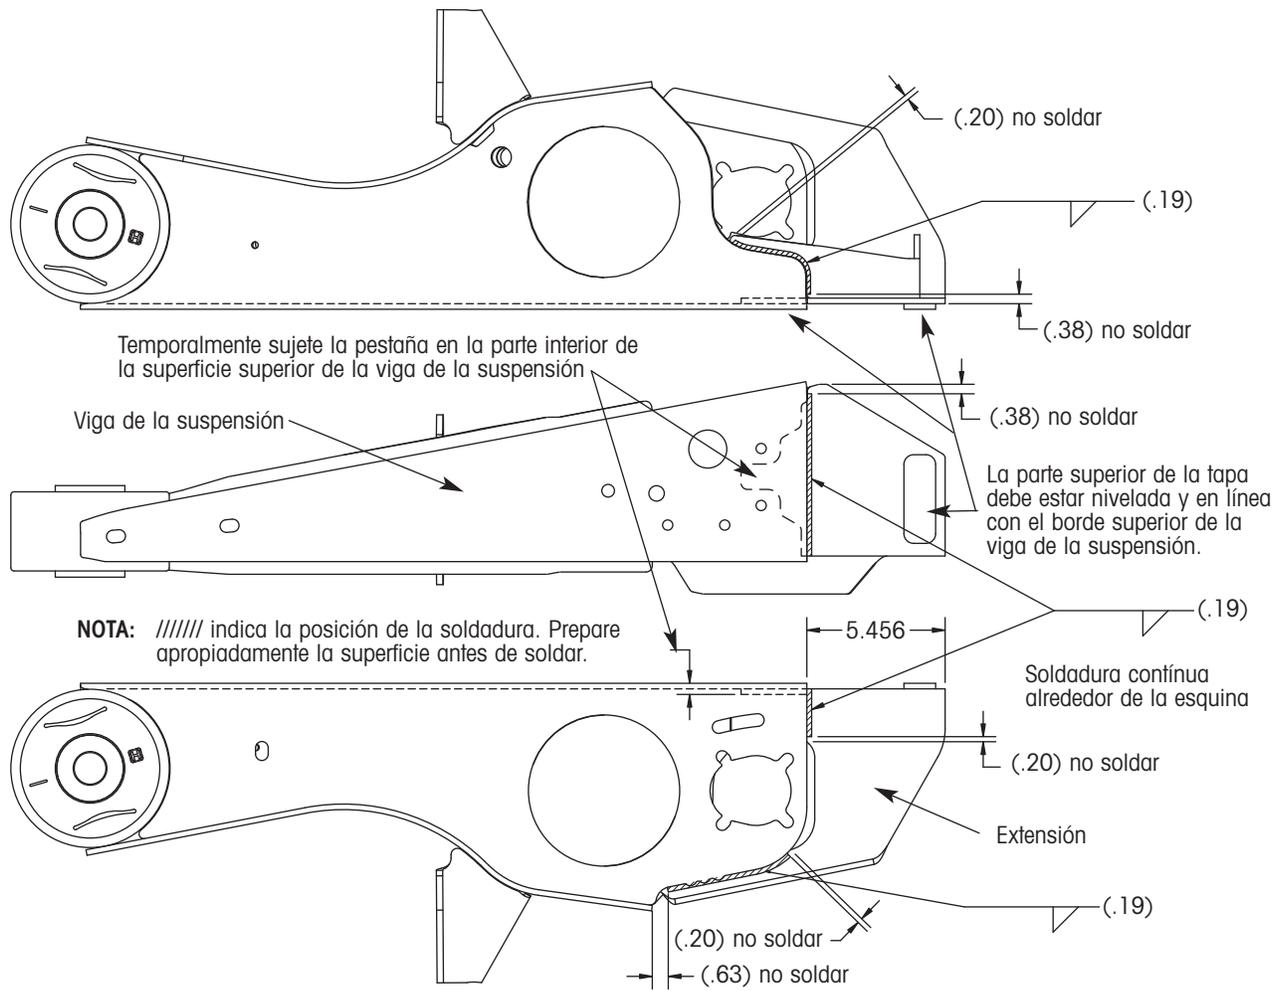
Preparación de las vigas de la suspensión para la soldadura e instalación de las extensiones de la viga
